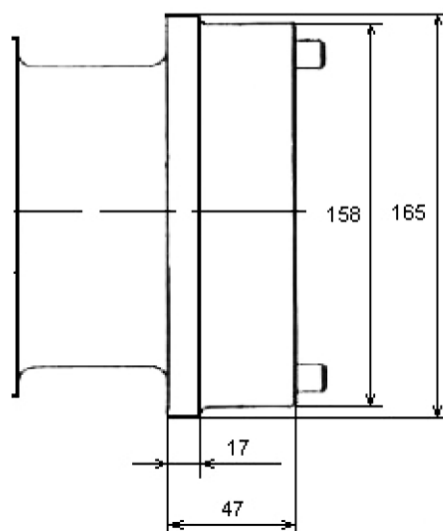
Кормовой участок коленчатого вала двигателя ЯМЗ-236
